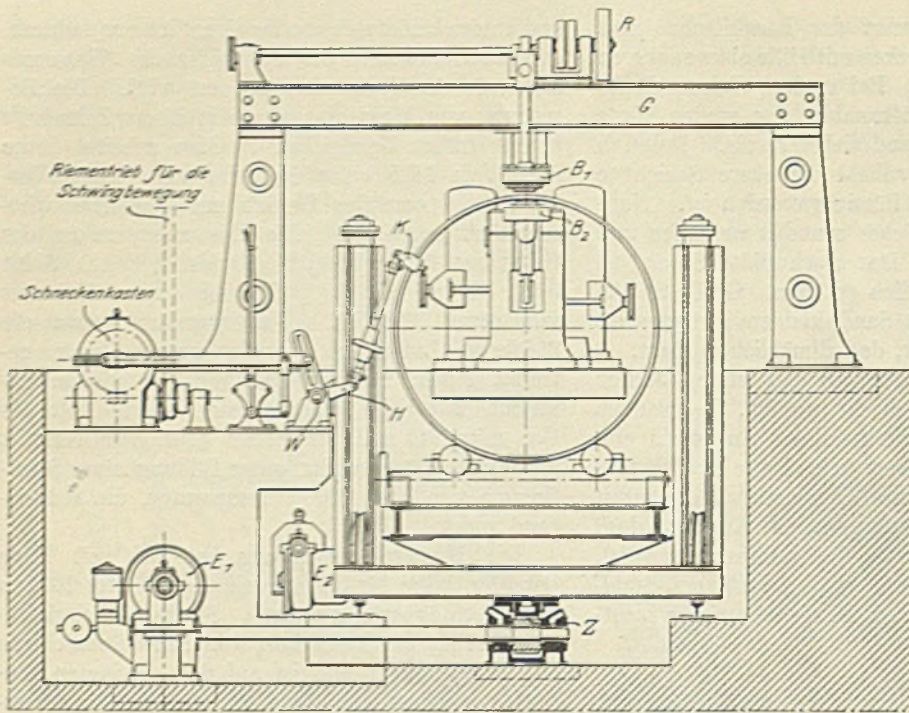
Hammerschweißmaschine mit Schwinghebelvorrichtung.
